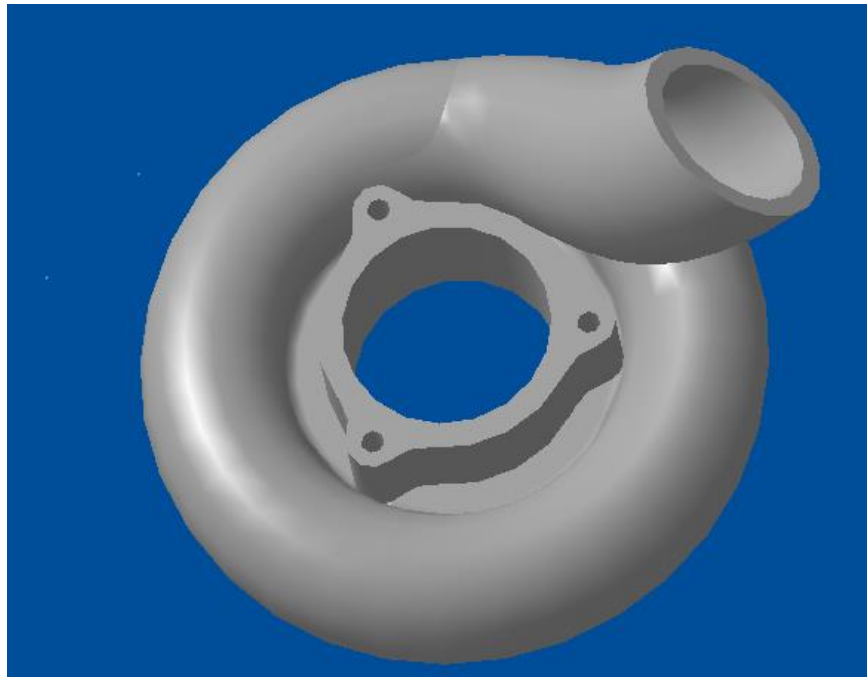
Кінцевий результат обробки деталі «Корпус компресора»
